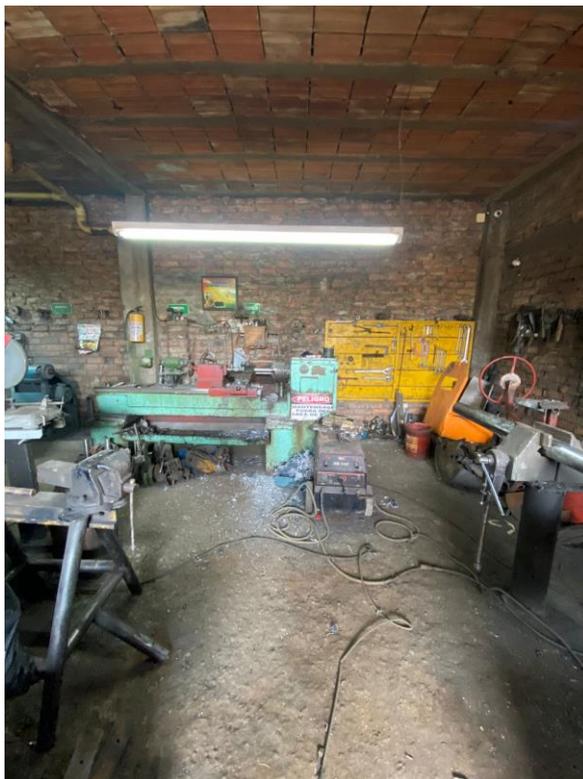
Foto Zona De Montaje 2. Fuente Autor
